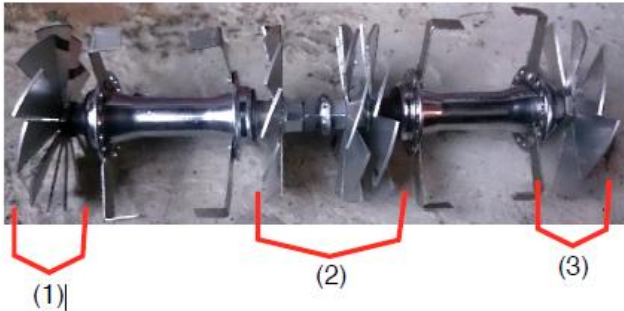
Montaje final sobre el eje de la turbina sin fuselaje
